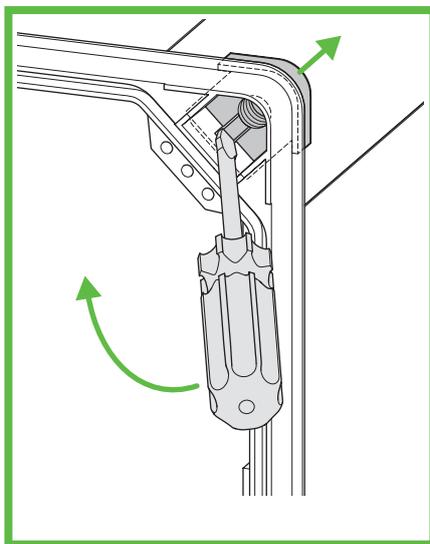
Gewindeeinschub heraushebeln (Ecke)
